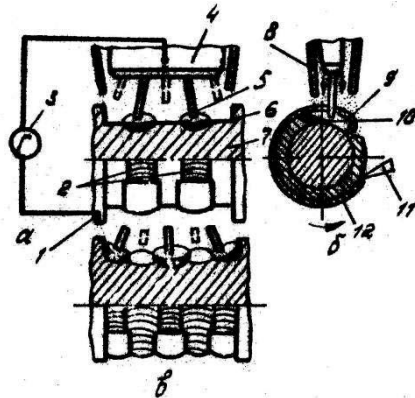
Схема багатоелектродного наплавлення в роздільні зварювальні ванни: а – наплавлення першої групи  $n$  валиків; б – видалення шлакової кірки; в – наплавлення другої групи  $n+1$  валиків; 1 – струмопровід; 2 – наплавлені валики; 3 – джерело струму; 4 – мундштук; 5 – електрод; 6 – зварювальна ванна; 7 – шийка вала; 8 – флюсопідвід; 9 – газовий пузир, 10 – розплавлений метал; 11 – скребок; 12 – шлакова кірка
